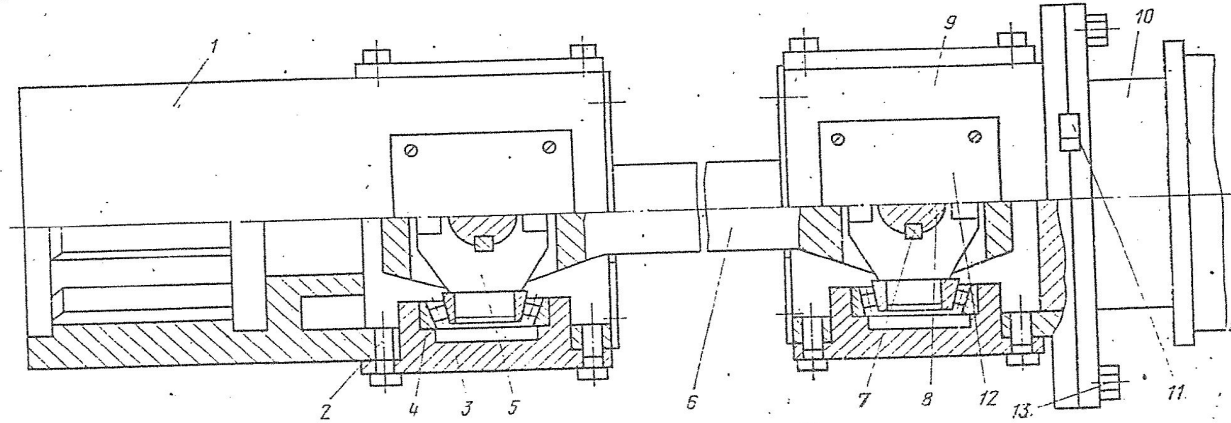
Универсальный шпиндель на подшипниках качения
